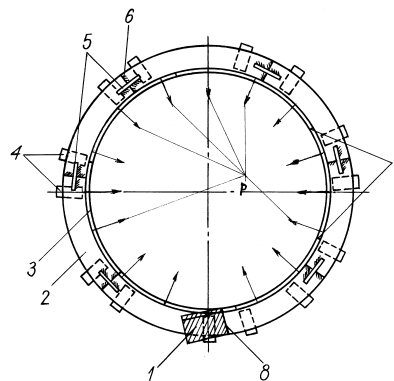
Схема крепления элементов ребер жесткости при сборке под сварку и действия расчетной нагрузки:
